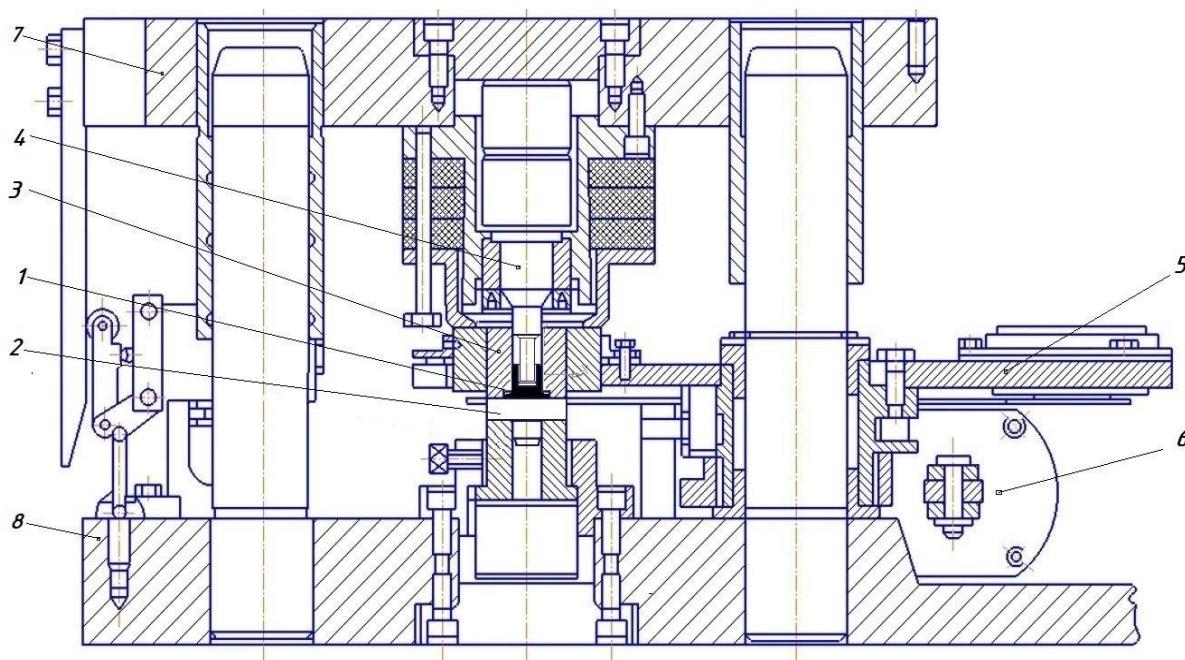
Штамп для виготовлення деталі типу стакан з фланцем з револьверною подачею
